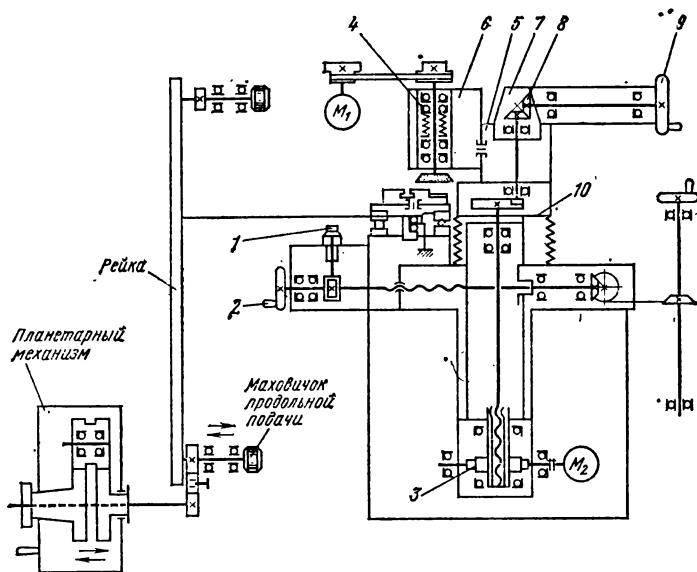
Кинематическая схема станка мод. 3М642Е:
